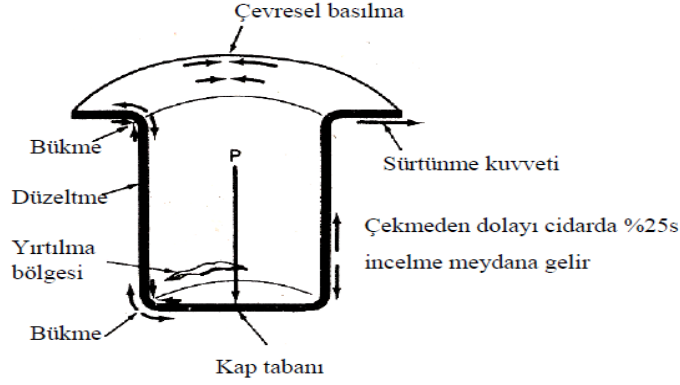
Derin çekmede meydana gelen gerilmeler.
